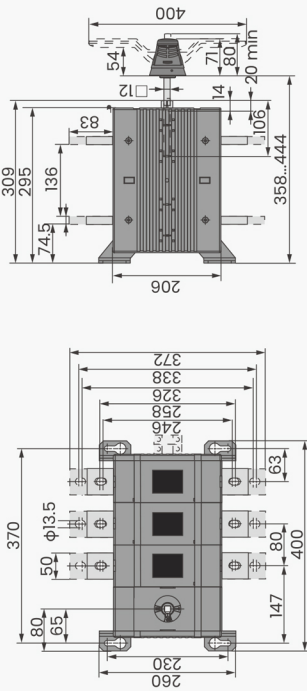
Габаритные и установочные размеры реверсивных рубильников 1000-1600А
